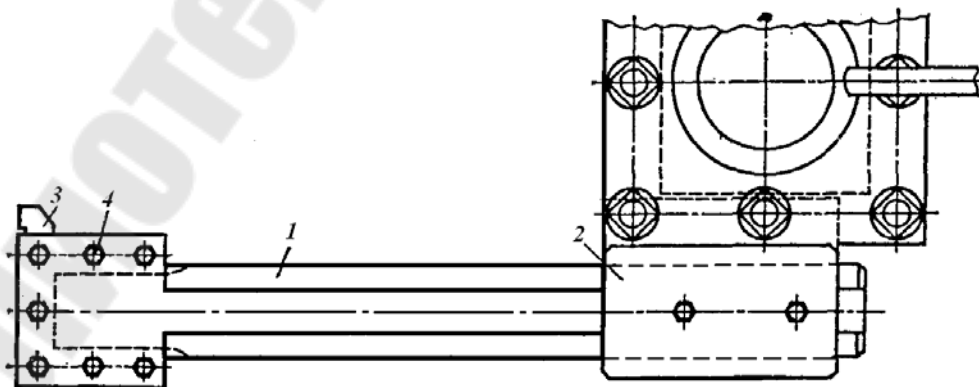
Резцовая оправка для обработки деталей над выемкой в станине
